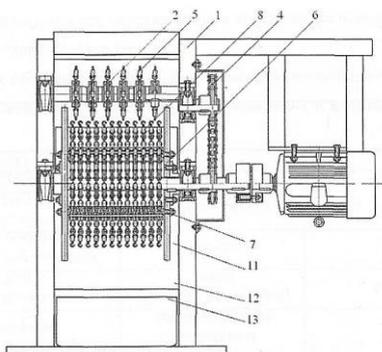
Устройство для заготовки хвойной лапки (вид спереди)
